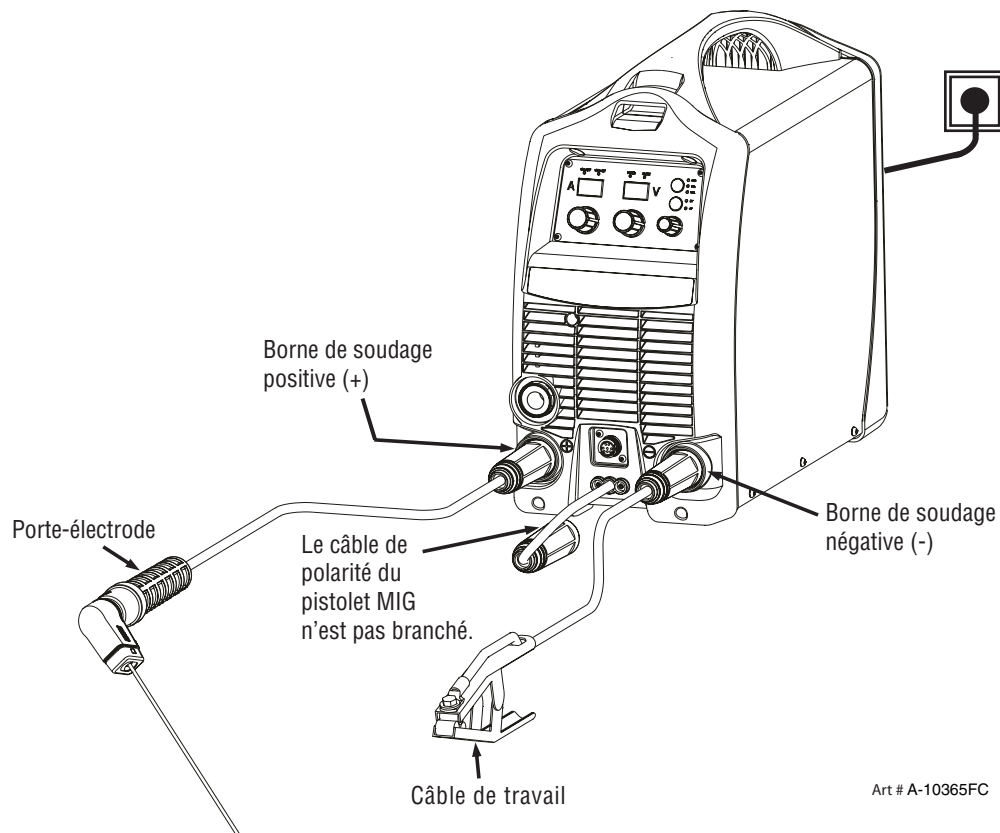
Configuration pour soudage manuel à l'arc.
